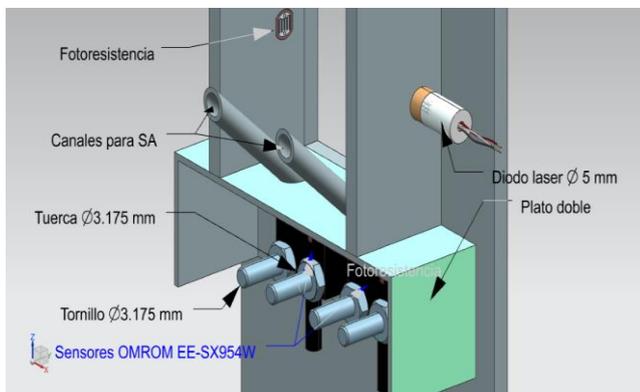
Dibujo de ensamble de SI con sensores EE-SX954W, PGM5626D y diodo laser.
